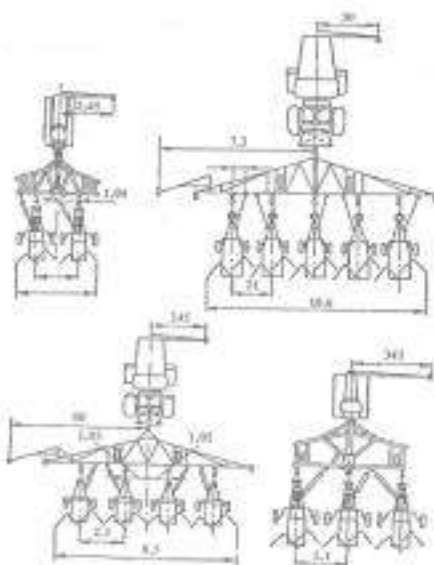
Разметка мест присоединения культиваторов – плоскорезов.
